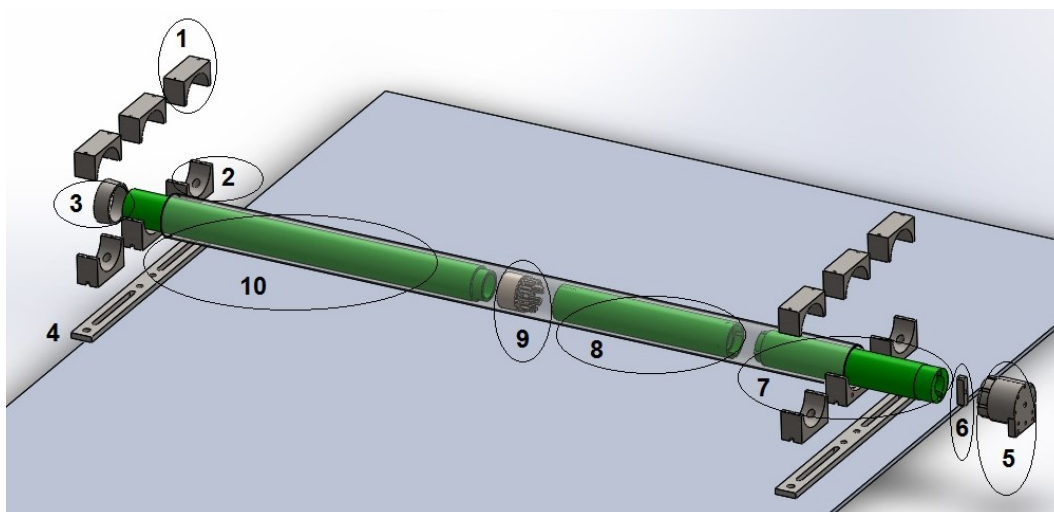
Vista explodida da montagem do sistema. Suporte superior de tubo (1), Suporte inferior de tubo (2), Centralizador de tubos(3), Base dos suportes (4), Fechamento de tubos (5), Conexão fechamento-tubo (6), tubo-fechamento (7), tubo-suporte sensores (8), suporte sensores (9), tubo PPR (10).
